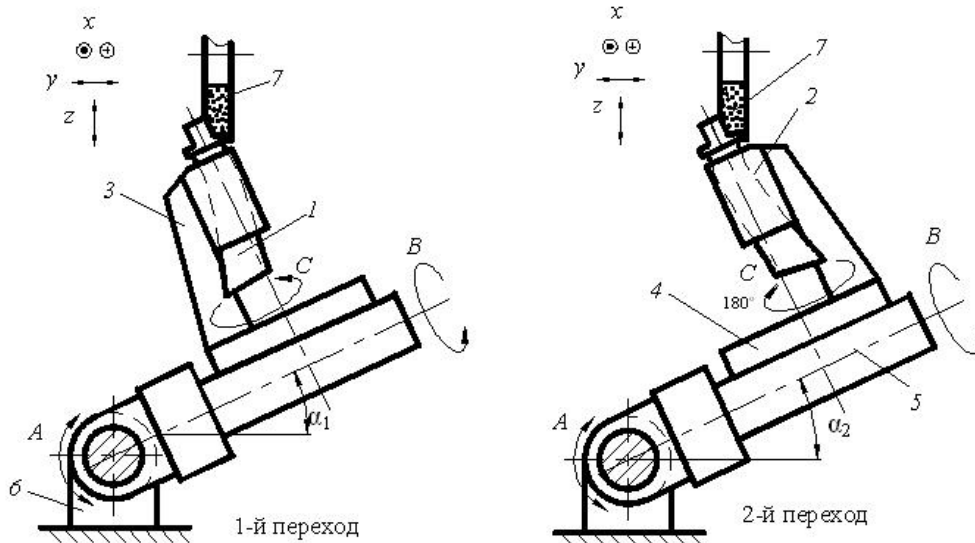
Схема взаимных перемещений инструментов и заготовки при шлифовании хвостовика рабочей лопатки 1-й ступени компрессора двигателя SaM-146 (1 и 2 переходы)
